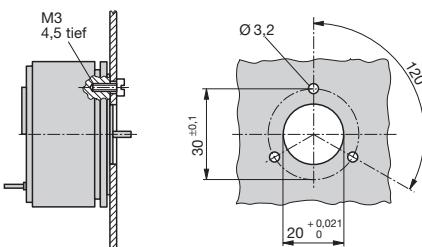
Bohrplan für Befestigung mit 3 Zylinderschrauben M3.
